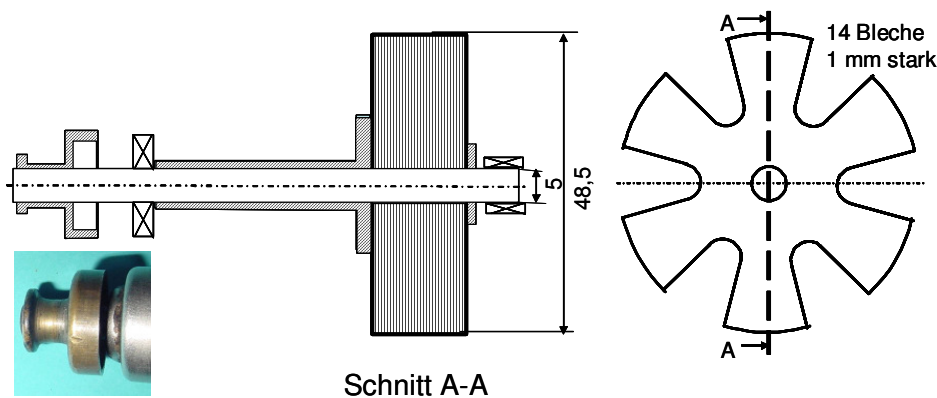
Längs- und Querschnitt des Dauermagnetläufers
